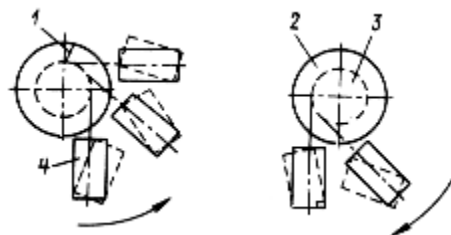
Рабочее положение искателя при поиске трещины: 1 - трещина; 2 - головка заклепки; 3 - заклепочное отверстие; 4 - искатель
